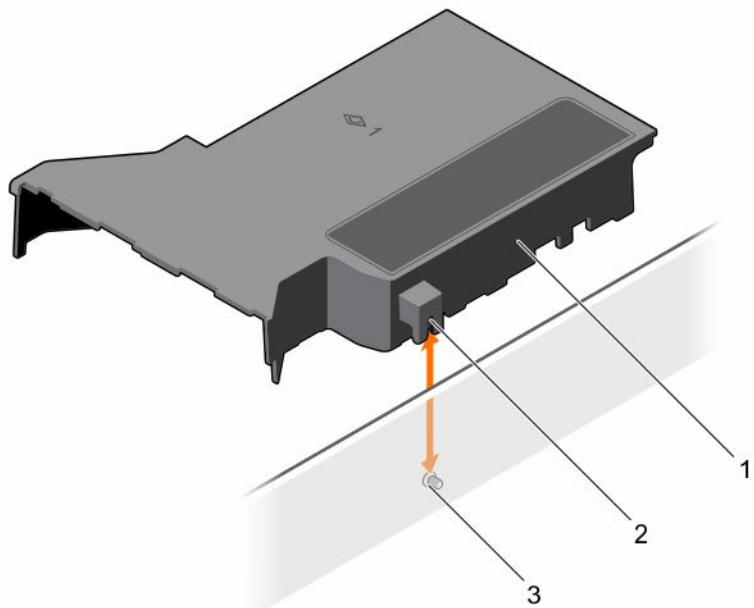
Extracción e instalación de la cubierta de refrigeración
